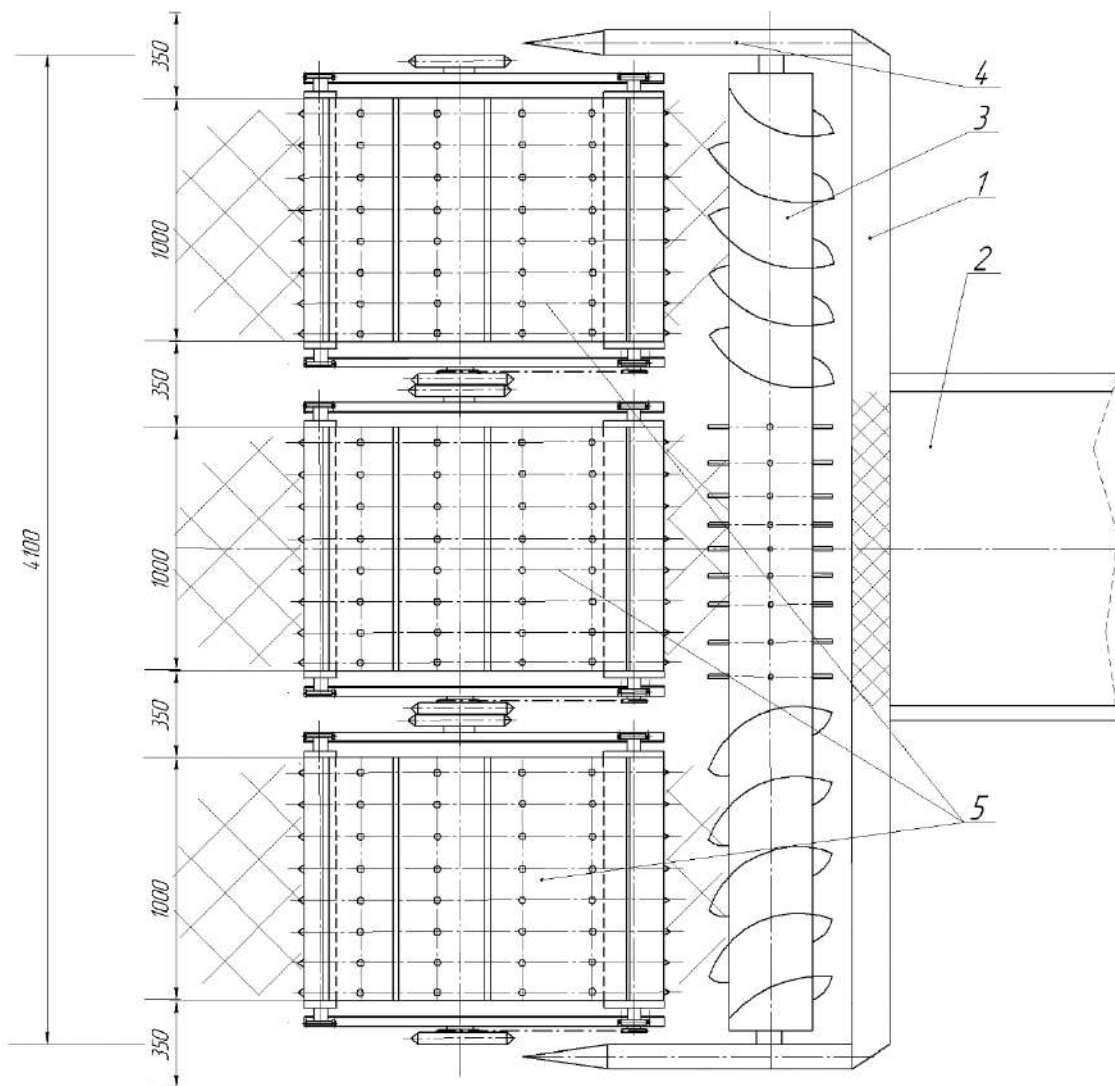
Комплектування жатки зернозбирального комбайна з підбиральним вузлом: 1 – корпус жатки; 2 – похила камера; 3 – шнек жатки; 4 – боковина; 5 – підбиральний вузол
